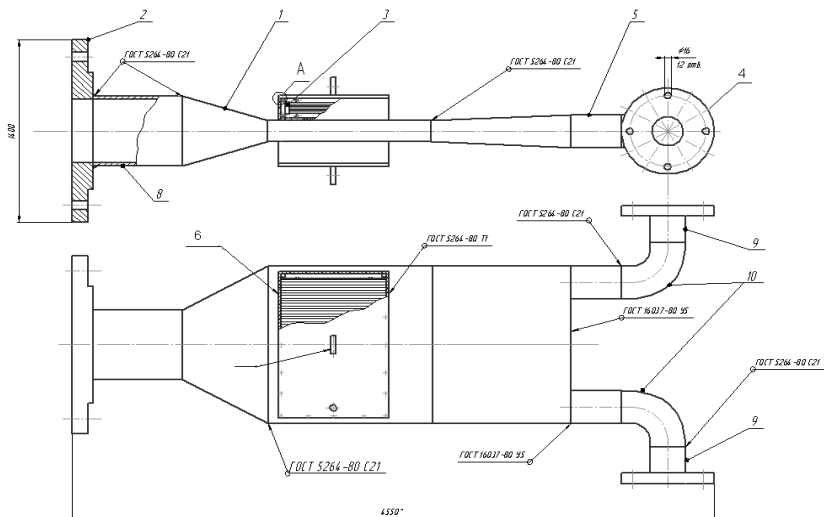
Установка электроактивации. Аппарат состоит из: 1 — корпуса, изготовленного из стали 12Х18Н10Т (ГОСТ 5632–72); 2 и 4 — фланцы из стали 12Х18Н10Т (ГОСТ 5632–72); 3 — магниты; 5, 8, 9 — патрубки; 6 — упорные бортики для закрепления магнитов; 7 — крышка из нержавеющей стали; 10 — отводы
